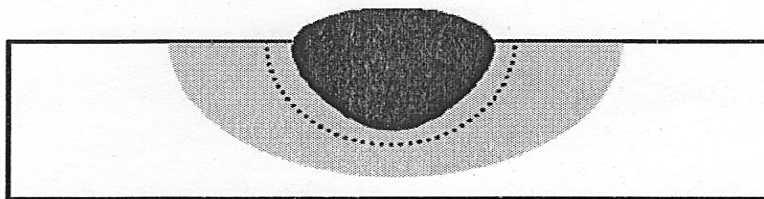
Утворення твердості наплавленого валика на сталі Soldur 7001
